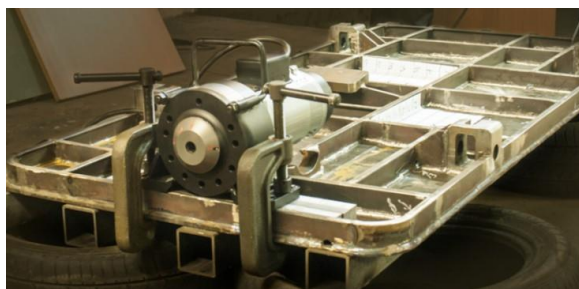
Снятие напряжения сварного шва вибрацией
